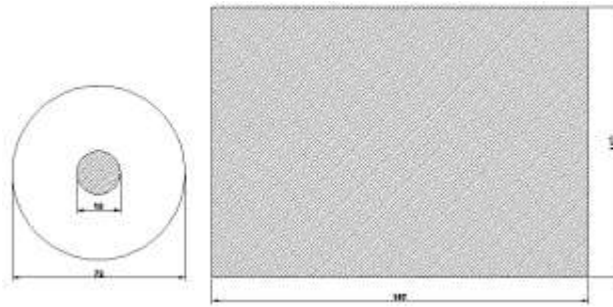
Dimensiones del carrete. Diseño de carrete para bobinado de electro imán.
